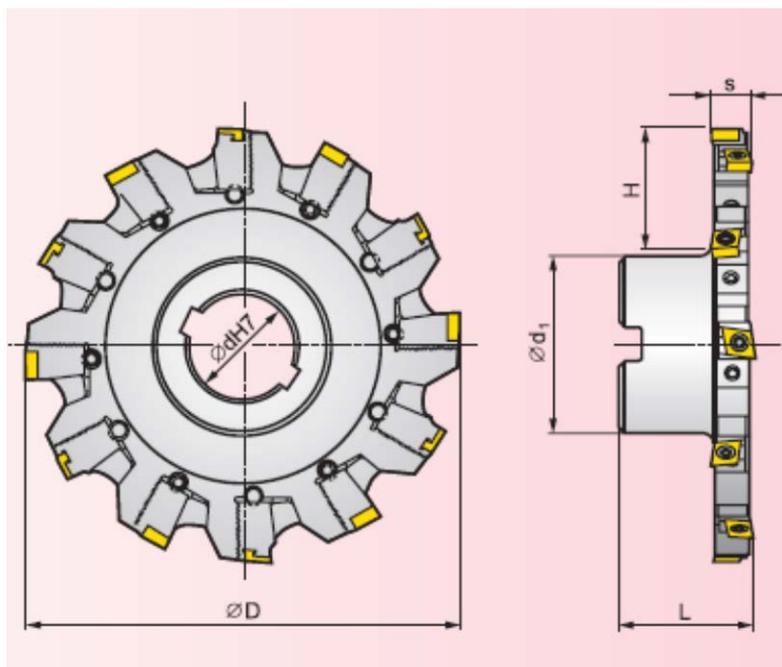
Фреза дисковая 160B06R-S90CN10N18
